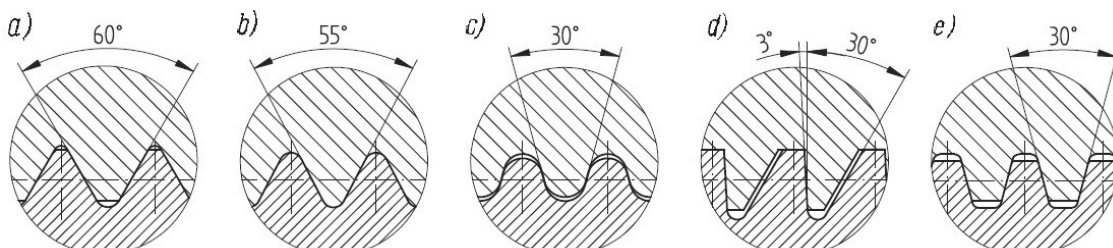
Gewinde-Grundformen. a) metrisches Gewinde, b) Whitworth-Gewinde, c) Rundgewinde, d) Sägewinde, e) Trapezgewinde<sup>82</sup>
